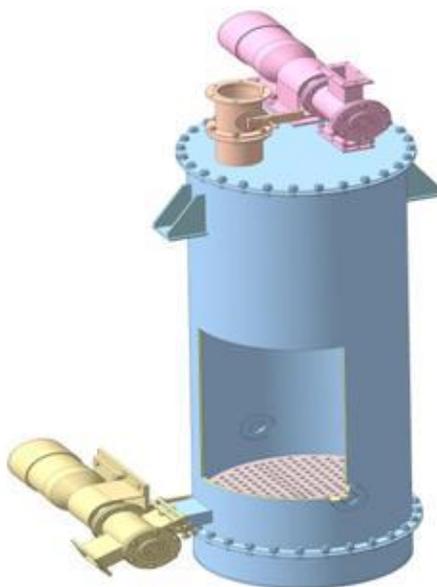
Циліндрична сушарка з киплячим шаром.
